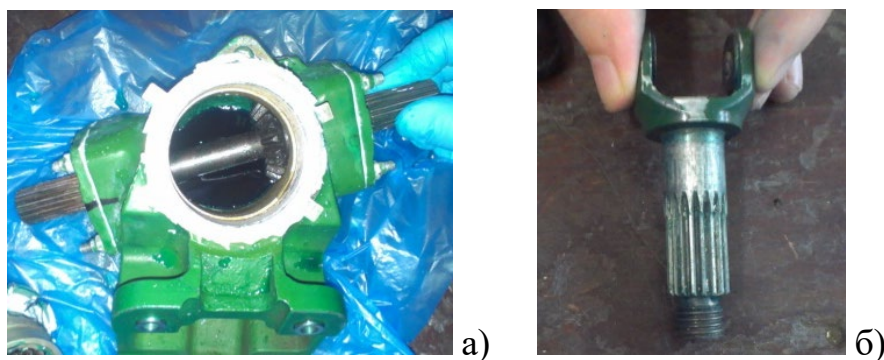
Кутовий редуктор: а) – корпус редуктора з валом-шестернею, б) – карданний вал шестерні 5.
